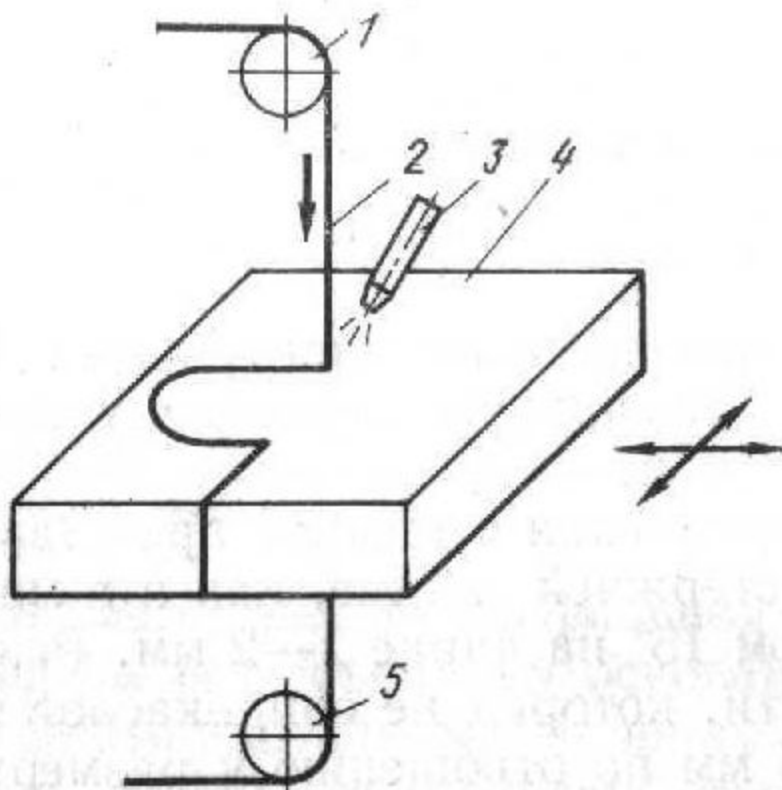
Схема изготовления матрицы с прямолинейными образующими на электроэрозионном вырезном станке: 1 — подающая катушка; 3 — сопло для подачи рабочей жидкости; 2 — элек-
